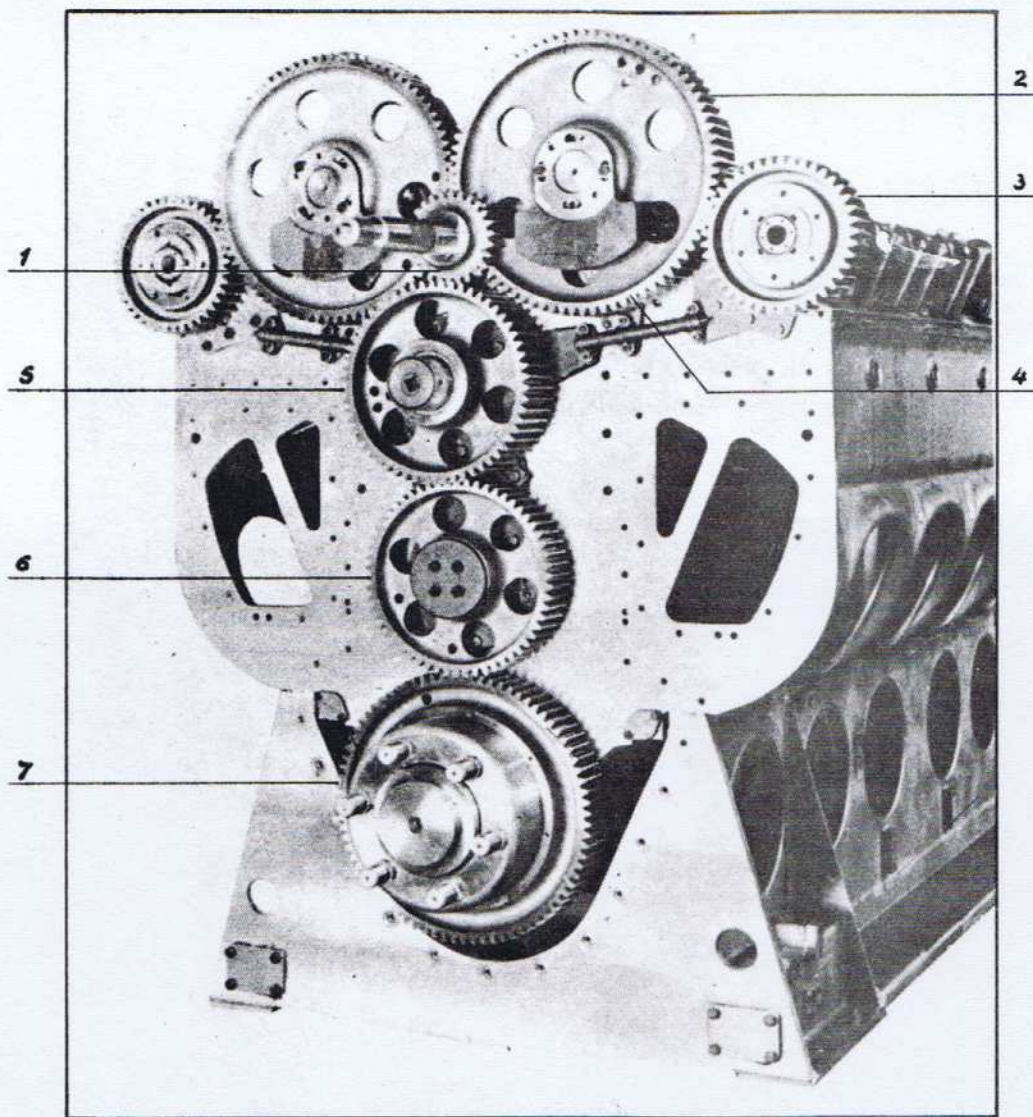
Carter du moteur GM 567C (Vue du dessous).
